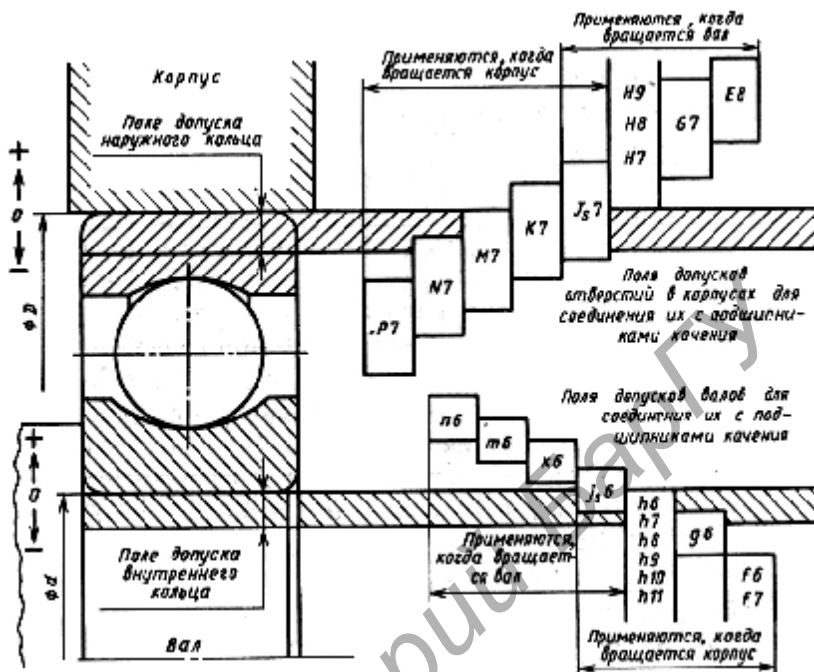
Схема расположения полей допусков на внутренний и внешний диаметры подшипников качения (на вал и в корпус)
